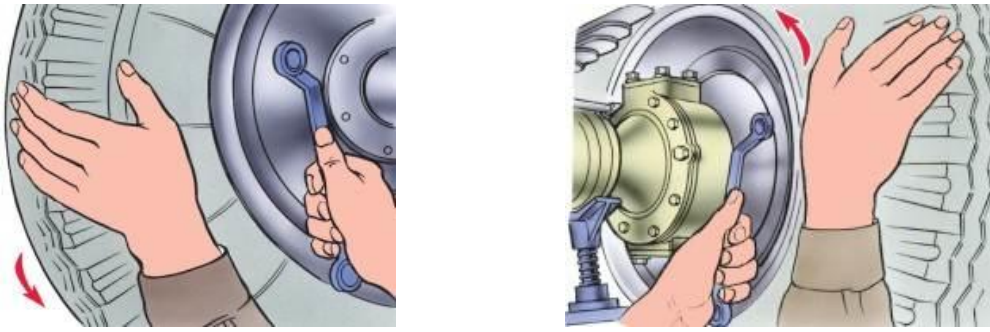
Регулировка зазора между колодками и тормозным барабаном
